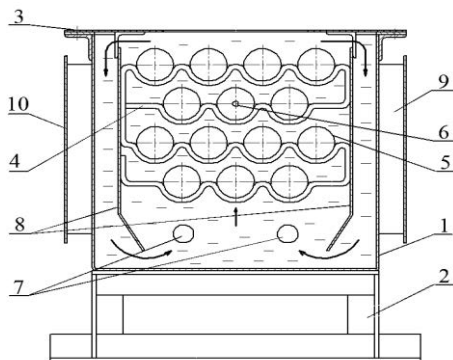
Електричний термоакумулятор: 1 - корпус; 2 - підставка;
